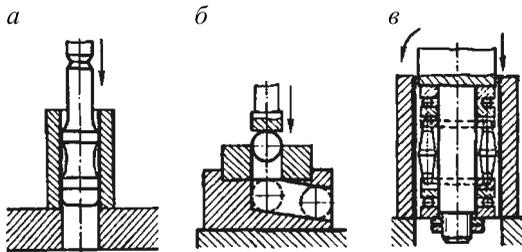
Схемы обработки отверстий без снятия стружки
